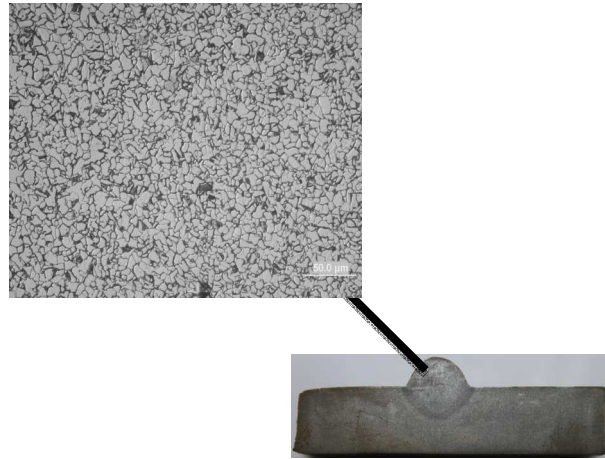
Структура сварного шва сварки в среде углекислого газа с применением модификаторов
